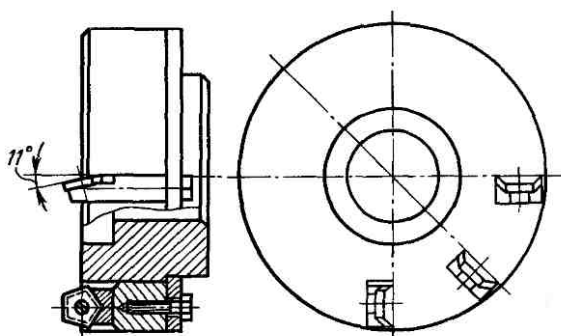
Фреза с пятигранными твердосплавными пластинами
